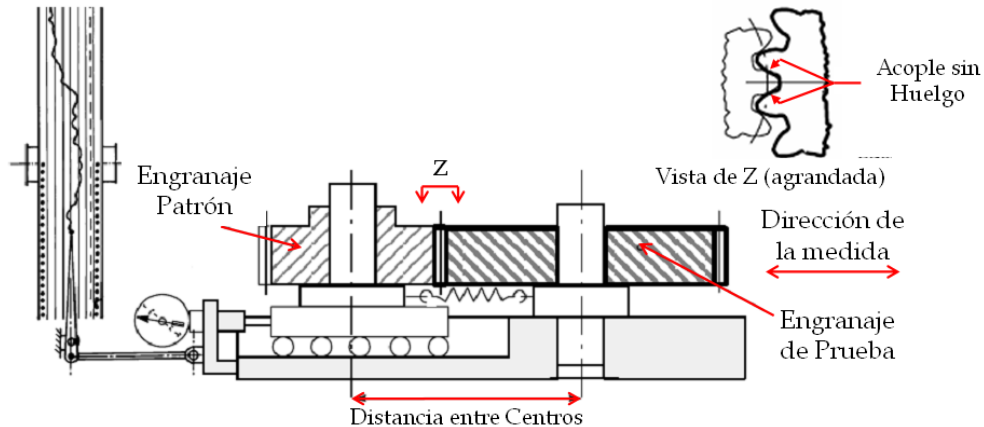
Esquema de Montaje del Dispositivo para la Prueba de Doble Flanco. Fuente: [13].
